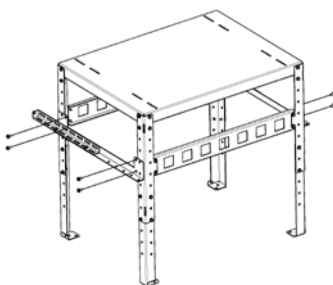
Assembleer de verstevigingen + de verlengstukken aan de structuur
